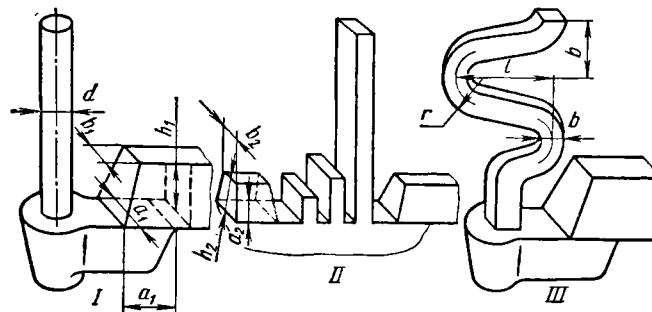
Конструктивные размеры стояков и коллекторов:
